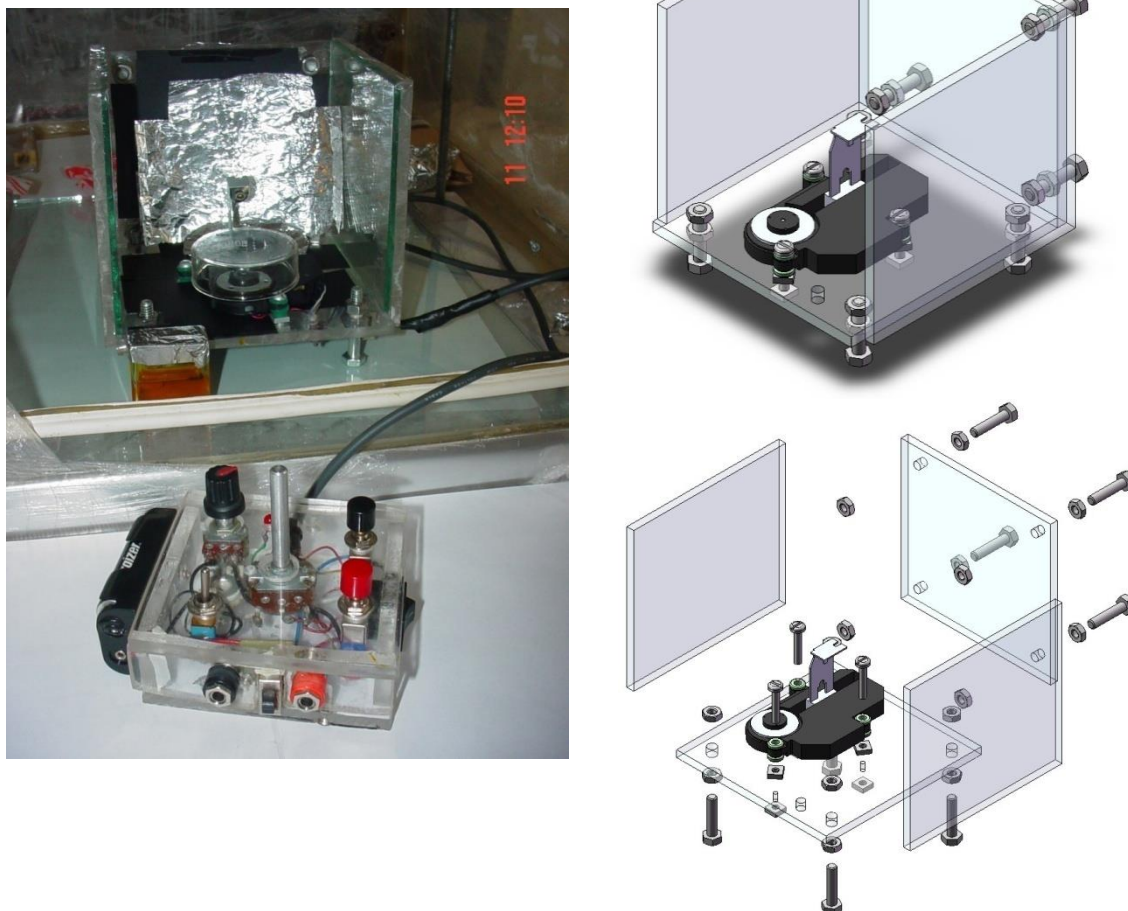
A la izquierda fotografía del EMFP y a la derecha vista isométrica explosionada del EMFP.
